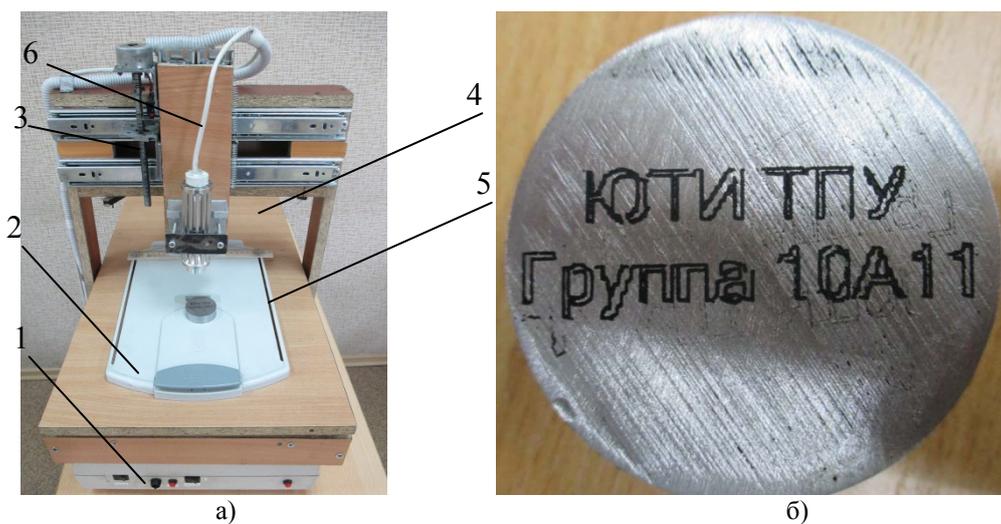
Общий вид станка с ЧПУ для маркировки лазером и образец с нанесенной маркировкой
